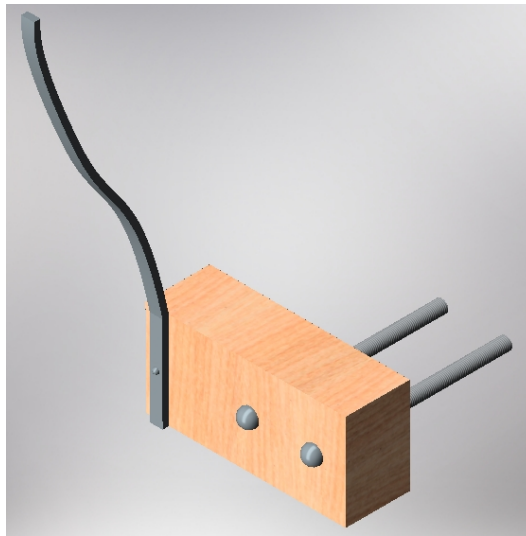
Perspectiva axonométrica del conjunto del sistema del indicador ensamblado.
